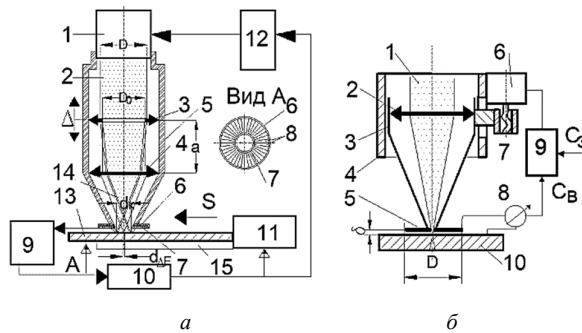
Схема пристроїв для автоматизації операцій поверхневої лазерної обробки: (а – для стабілізації процесу поглинання енергії випромінювання поверхню заготовки: 1 – лазер; 2 – промінь; 3 – лінза з отвором; 4 – об’єктив; 5 – корпус пристрою; 6 – металевий диск з чутниками 7; 8 – сектори чутників; 9 – вимірювач; 10 – процесор; 11 – механізм переміщення заготовки; 12 – блок живлення лазера; 13 – заготовка; 14 – сконцентрована частина променя; 15 – стіл технологічний; б – для стабілізації умов опромінювання в разі деформованих листових заготовок: 1 – промінь; 2 – об’єктив; 3 – корпус об’єктиву; 4 – корпус пристрою; 5 – металевий диск; 6, 7 – привод переміщення об’єктиву; 8 – вимірювач ємності конденсатору 5–10; 9 – тригер; 10 – заготовка)
